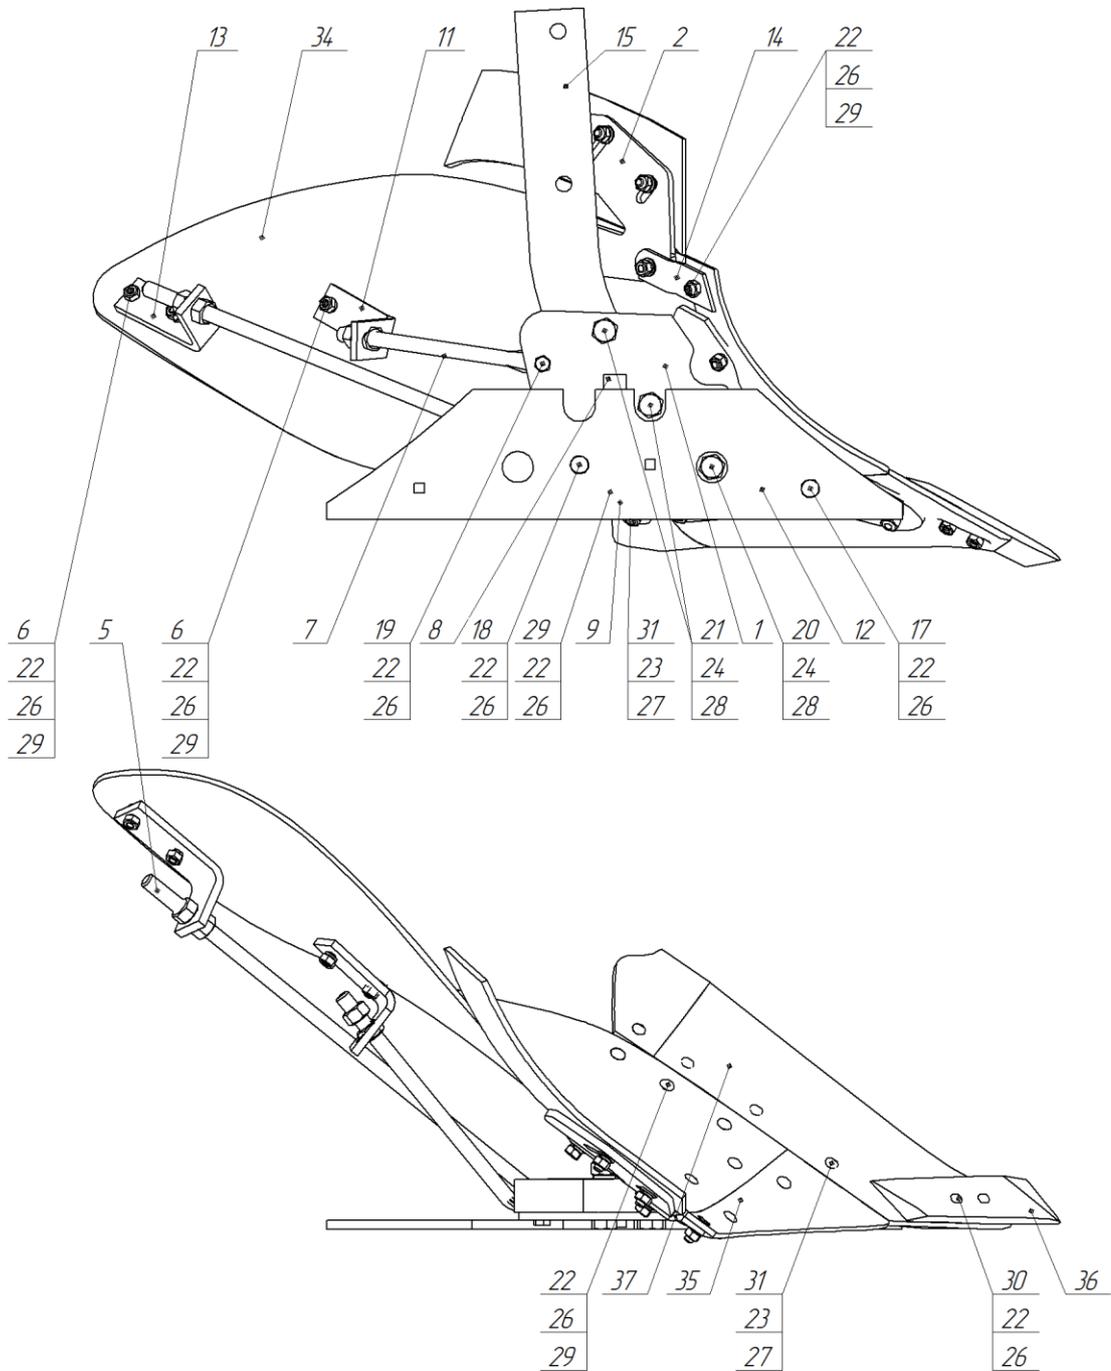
КСО-45 00.00.000-01 Корпус в сборе левый
